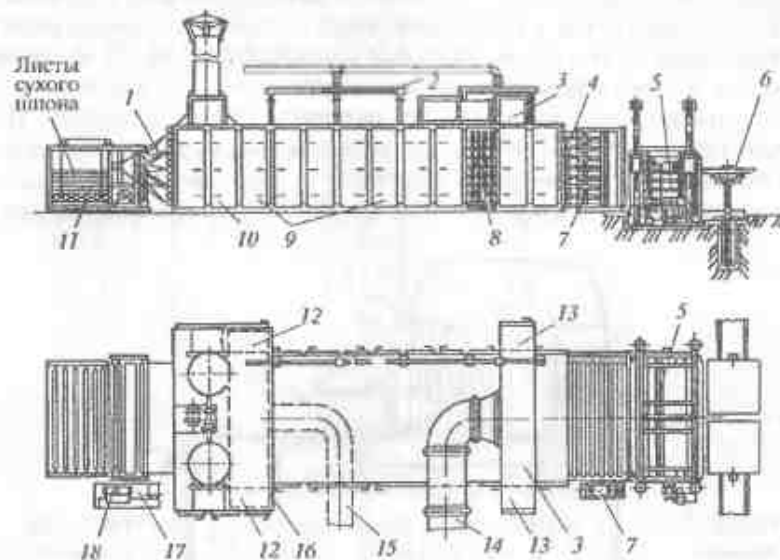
Общий вид газовой роликовой сушилки СРГ-25:
